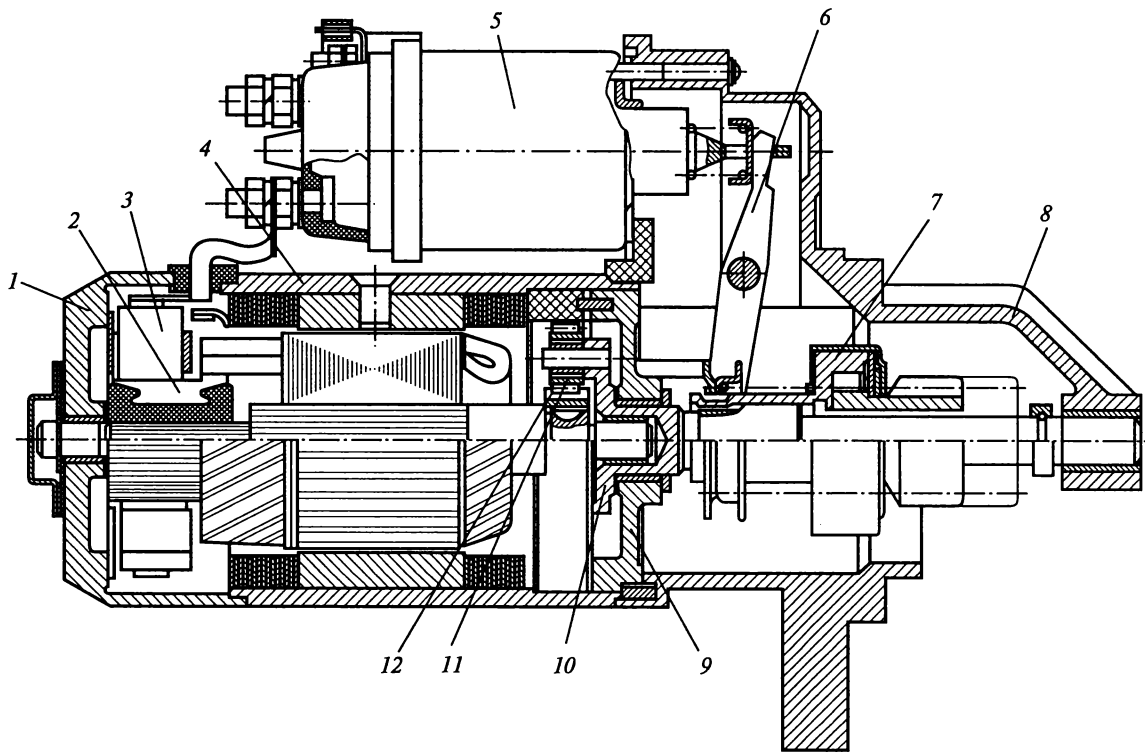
Конструктивная схема стартера с редуктором и электромагнитным возбуждением:
